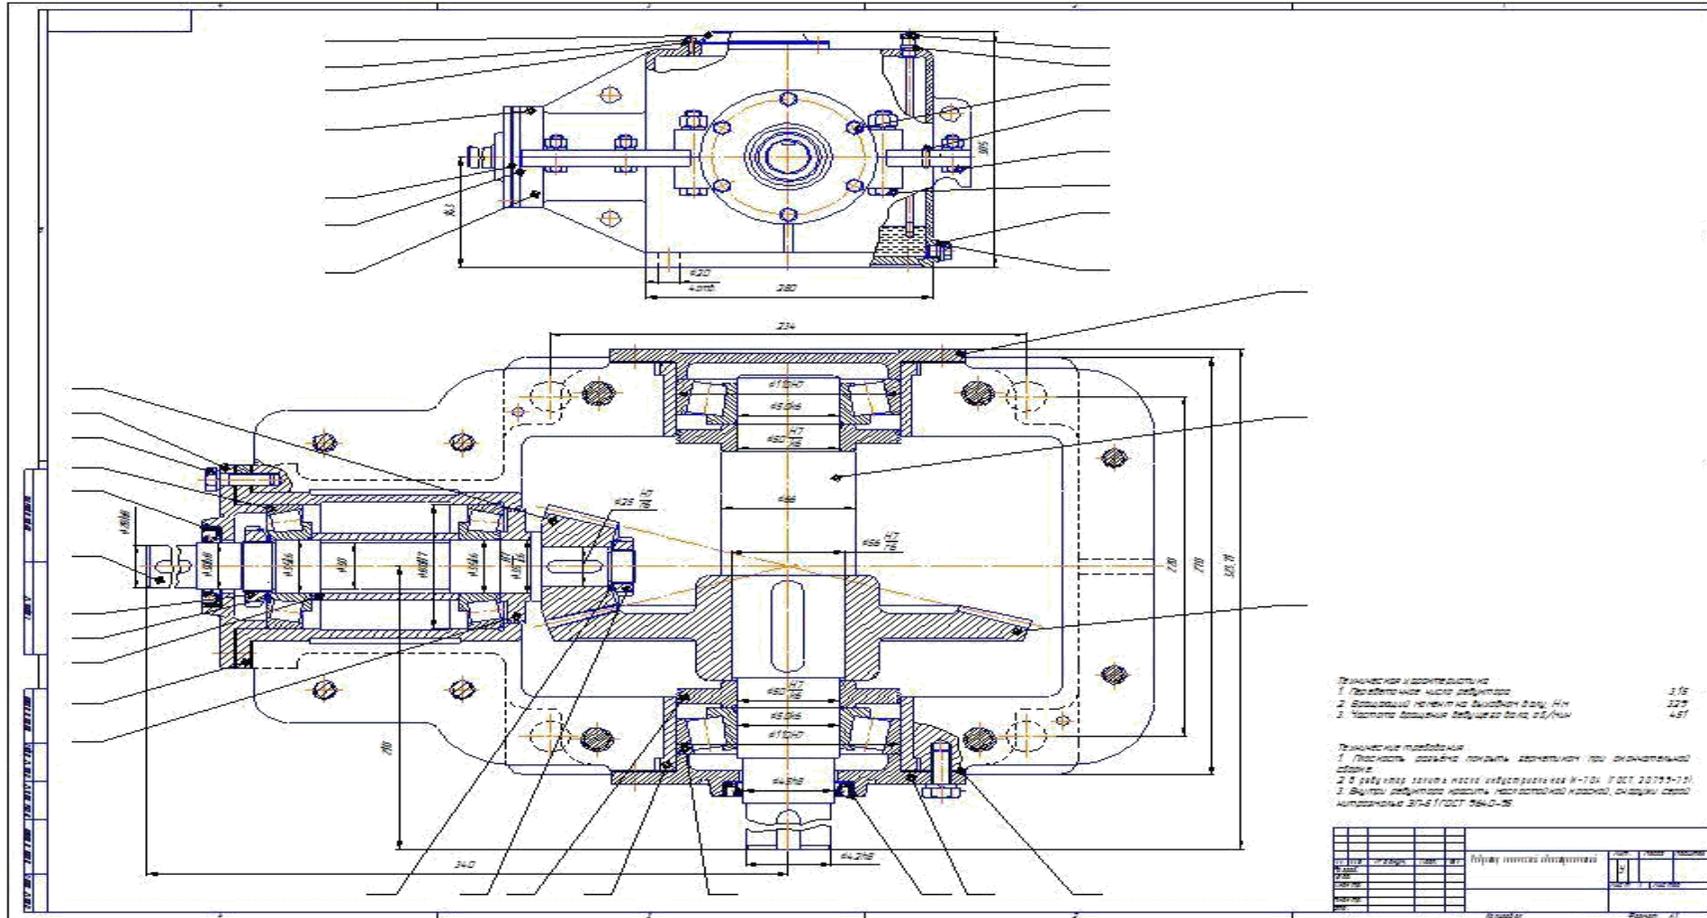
Цилиндрический одноступенчатый редуктор
